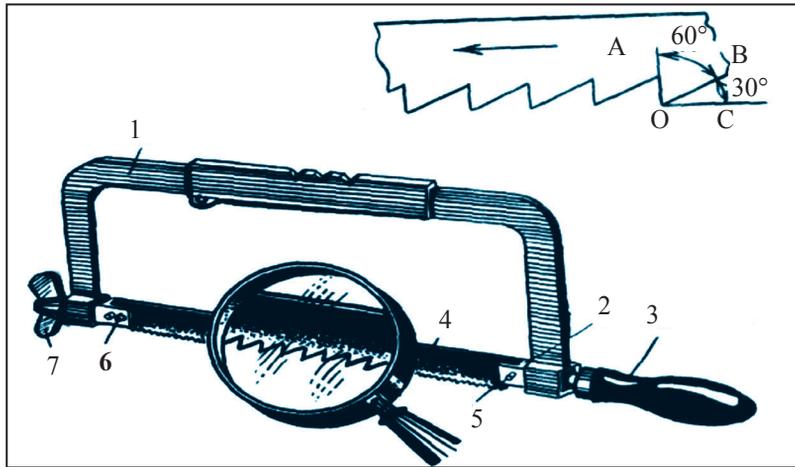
Ручная слесарная пила: 1 – основа (рамка); 2 – хвост; 3 – ручка; 4 – полотно пилы; 5 – штифт (металлический стержень); 6 – натяжной винт; 7 – гайка с ушками.
